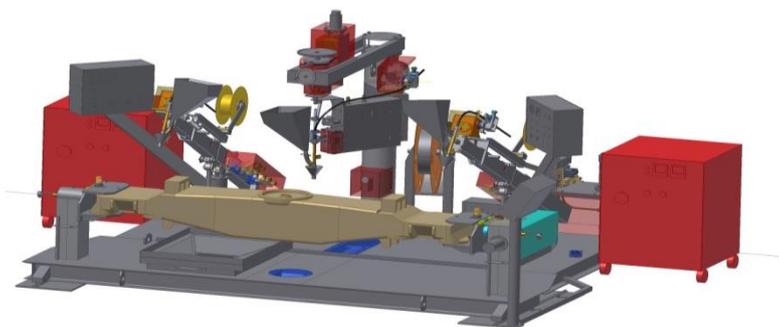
Установка для автоматической дуговой наплавки под слоем флюса
